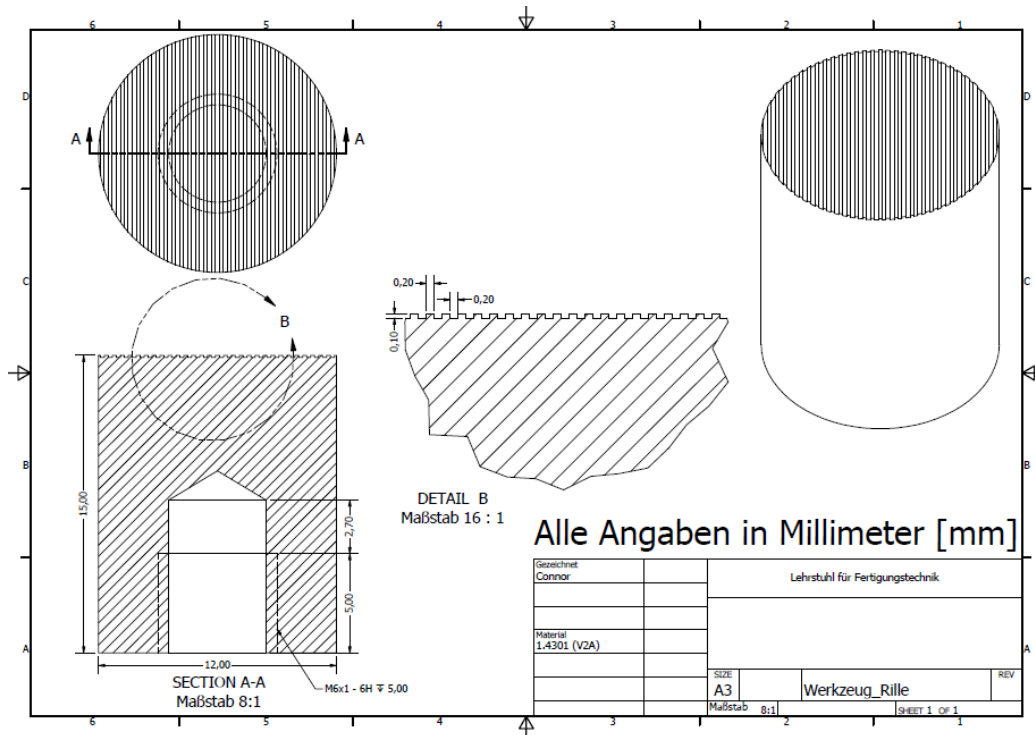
Technische Zeichnung des rillenstrukturierten Werkzeugs
